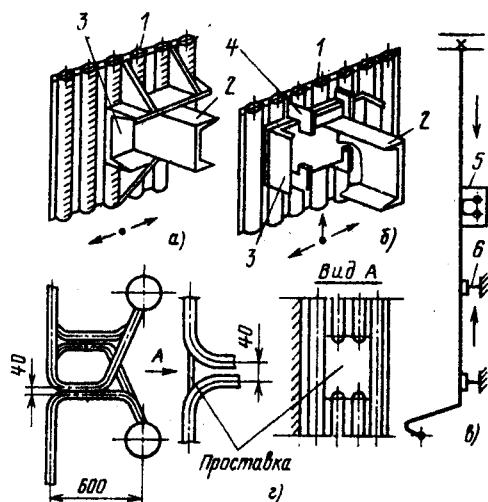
Конструкции крепления (а, б), подвески (в) и узла сопряжения (г) вертикальных панелей:
